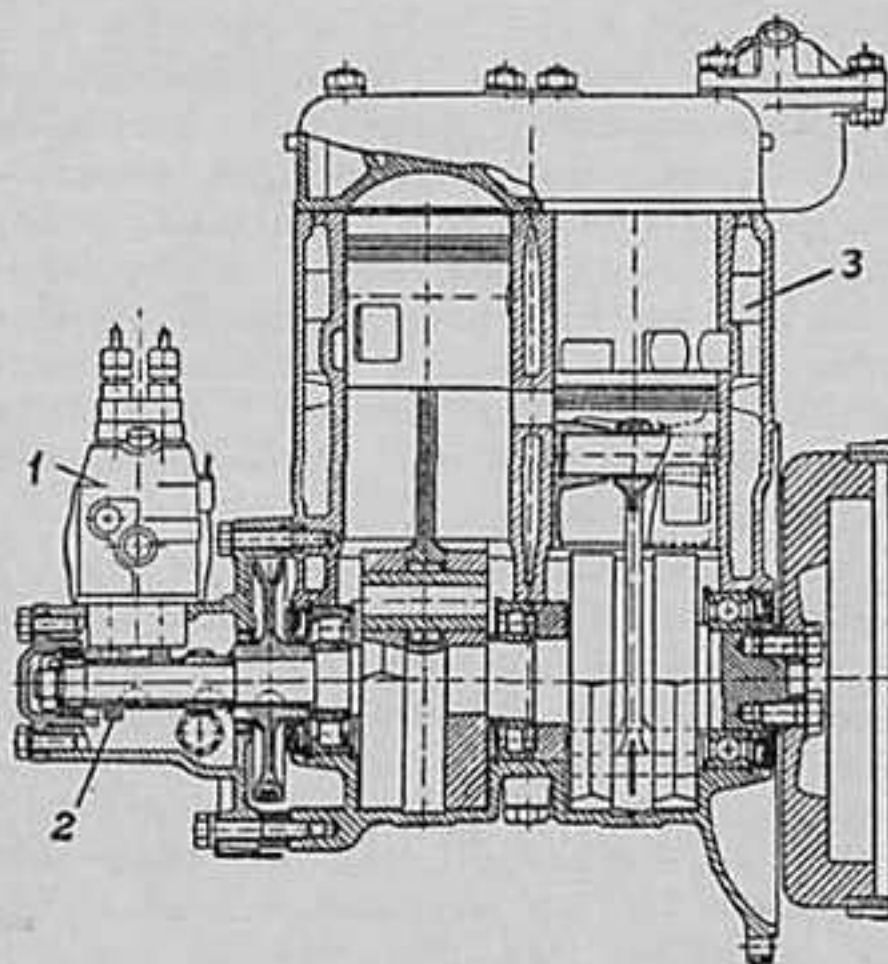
Двухцилиндровый двухтактный двигатель с впрыском бензина: 1 — двухплунжерный насос высокого давления, 2 — кулачки для привода плунжера насоса, 3 — двигатель.
